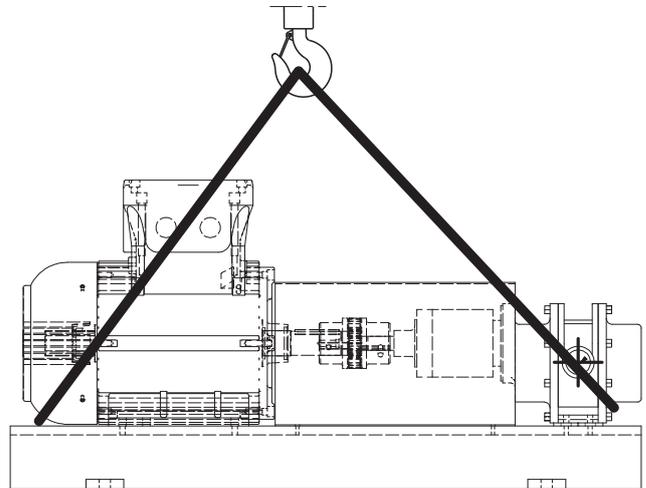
Hebezeug befestigen an Pumpenaggregat mit Grundplatte
